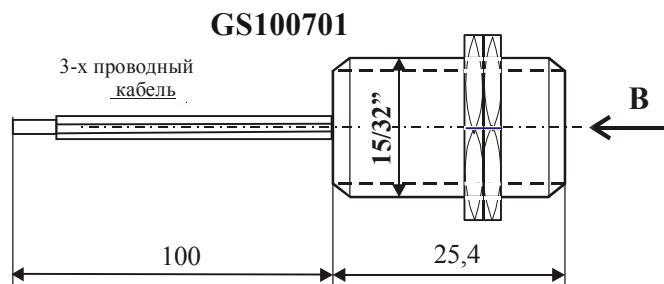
Внешний вид и габаритные размеры датчиков типа GS1007
